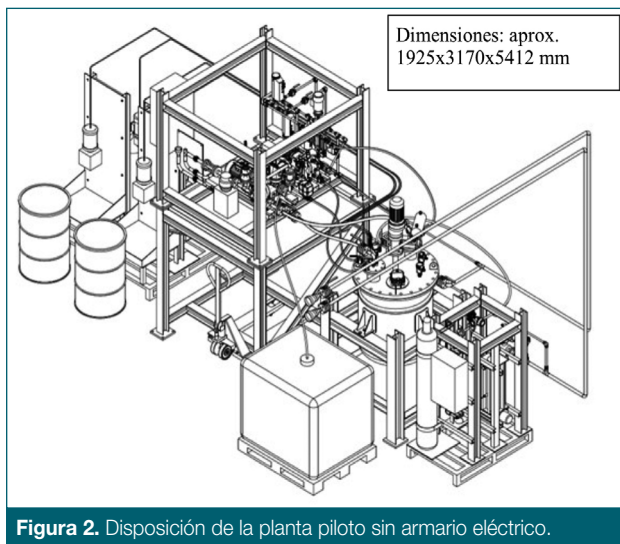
Disposición de la planta piloto sin armario eléctrico.
